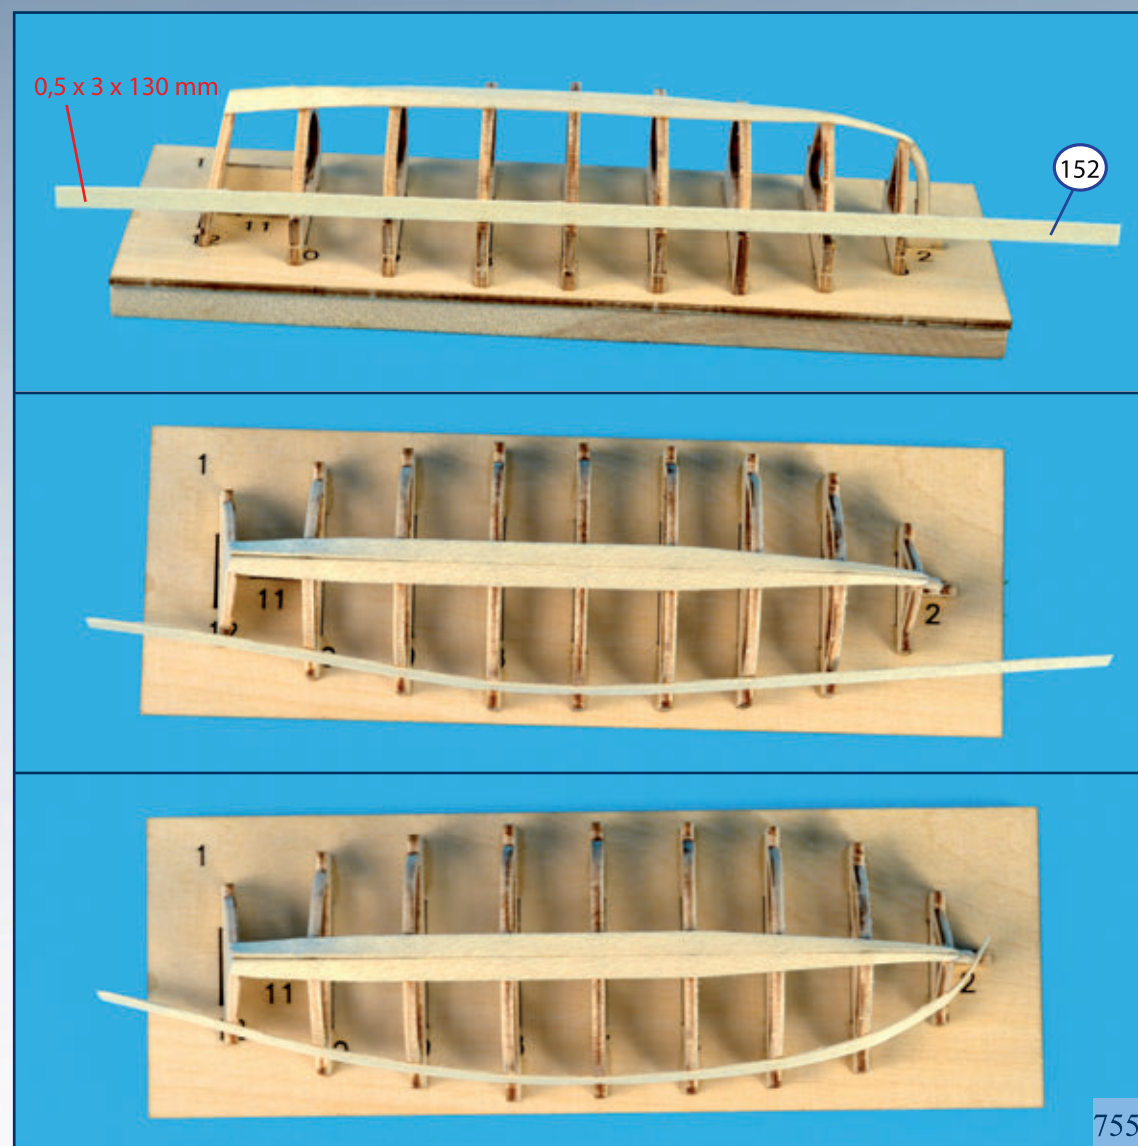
De una chapa 152 de 0.5x3x300mm corte una pieza de 130 mm de largo. Adáptela y péguela.
